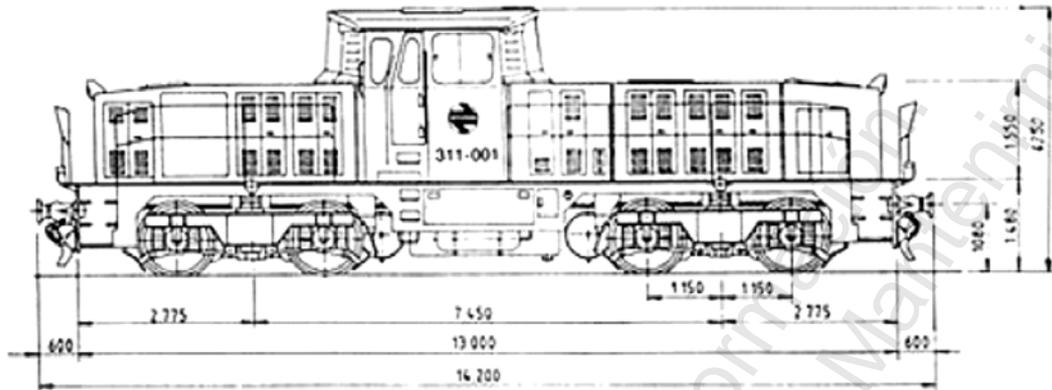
Dimensiones de la locomotora. S/ 311
